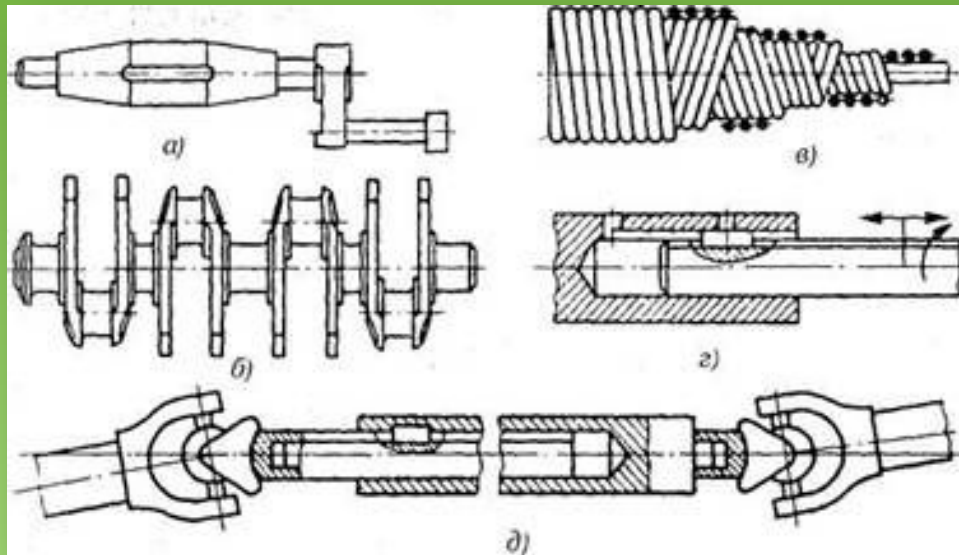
Типы валов: а — кривошипный вал; б — коленчатый вал; в — гибкий вал;
